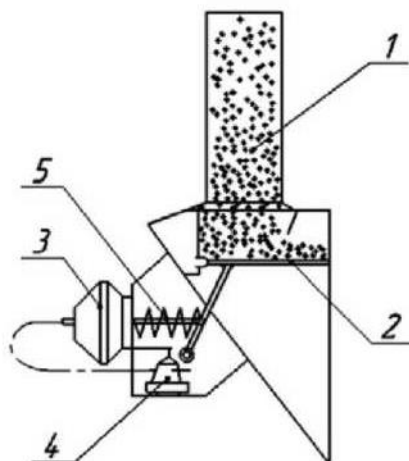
Шиберний дозатор доїльної установки УДА-16: 1 – приймальний бункер; 2 – шибер (заслінка); 3 – мембрана; 4 – пульсатор; 5 – поворотна пружина
